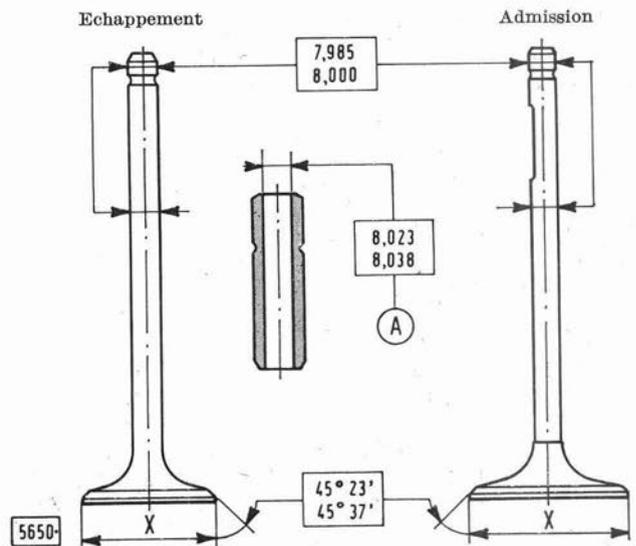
Dimensions principales en mm des soupapes d'admission, d'échappement et de leur guide.
